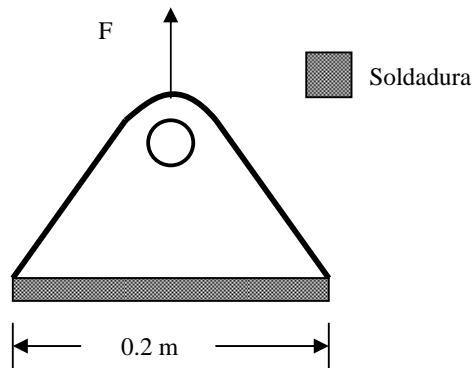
Soldadura en Oreja de jaula de inmersión.
